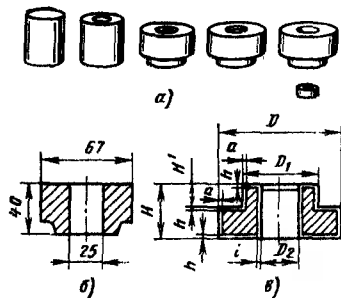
Заготовка зубчатого колеса, изготовления на многопозиционном автомате: а — последовательность горячей высадки; б — размеры заготовки; в — допуски и припуски на основные размеры заготовки
